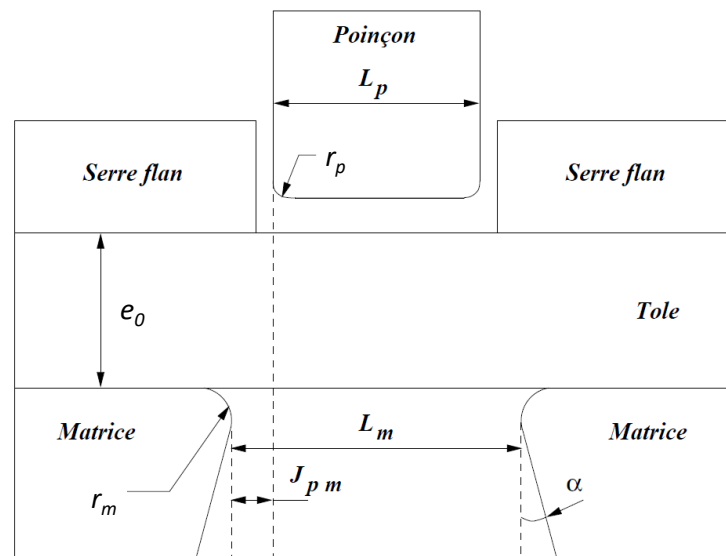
Dimensions des outils et paramètres technologiques d'une opération de découpage (adaptation de [11])
